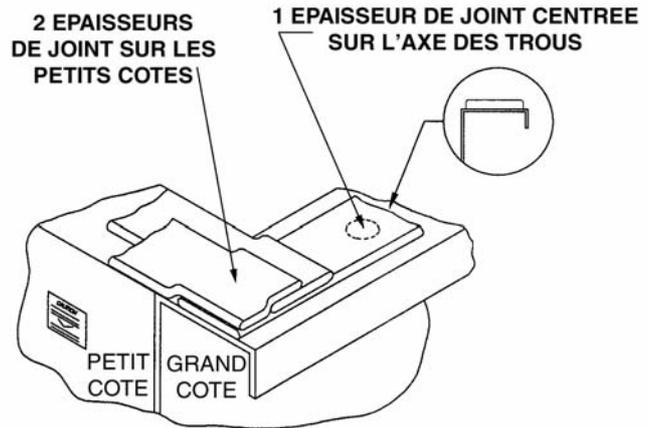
Pose du joint d'étanchéité sur la bride de la section bassin.
